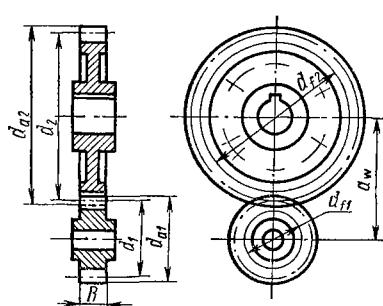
Цилиндрические зубчатые передачи, внешнее зацепление
